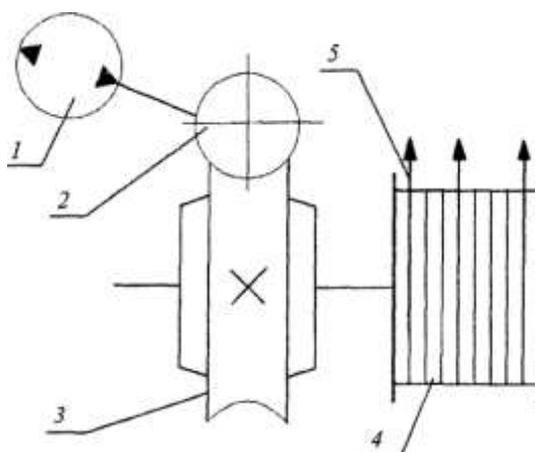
Механизм выдвигания лебедкой: 1 - гидромотор; 2 - червяк; 3 - червячное колесо; 4 - барабан; 5 - канат
